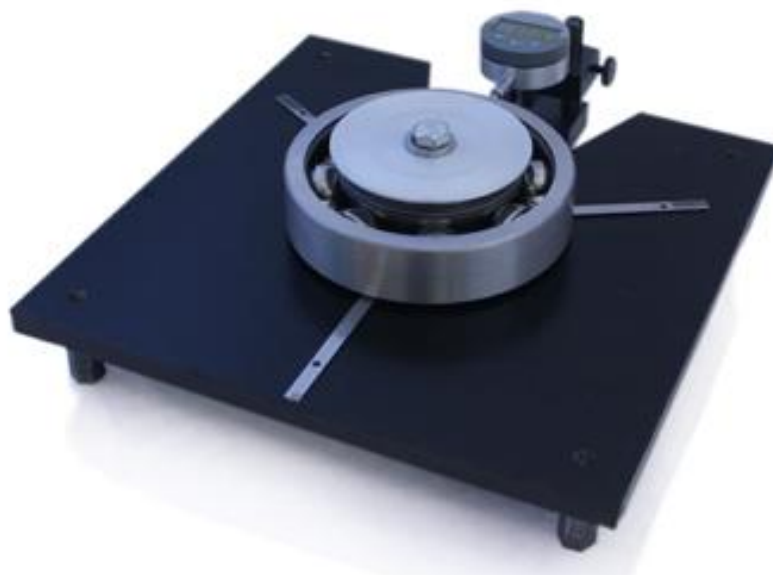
Пристосування для вимірювання радіального зазору підшипника
